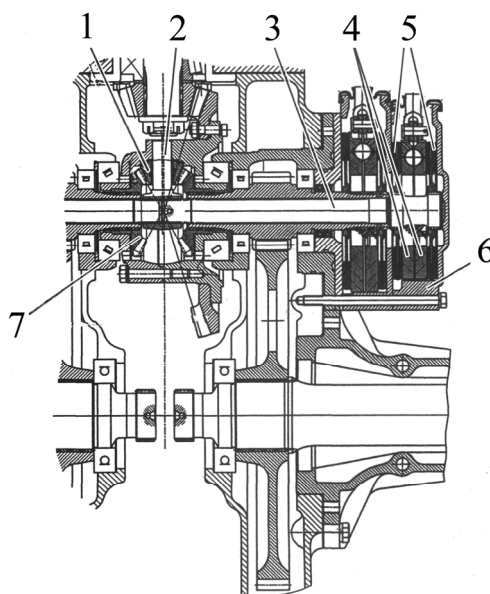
Регулировка управления рабочими тормозами
